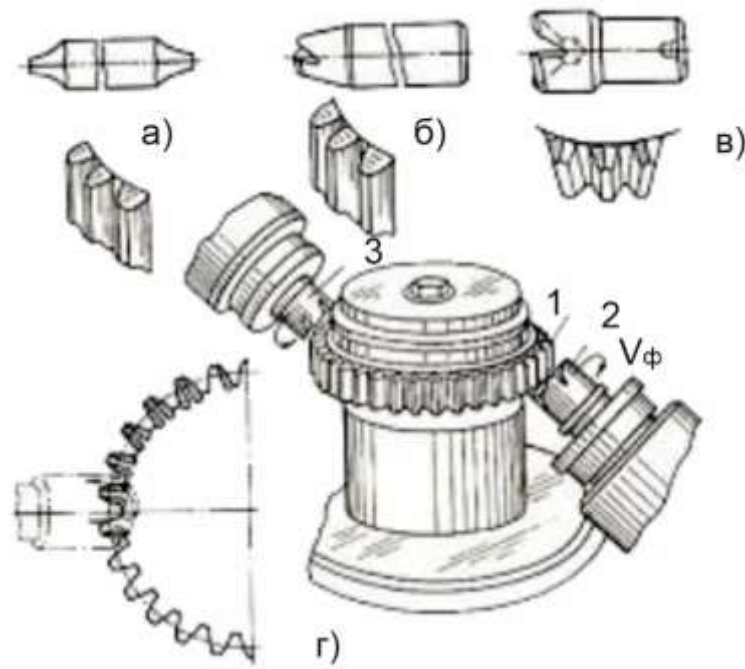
Варіанти закруглення зубів: а, б – пальцевою фрезою; в – чашковою фрезою; г - схема зубозакруглення чашковою фрезою; 1 – заготовка; 2 – фреза.
